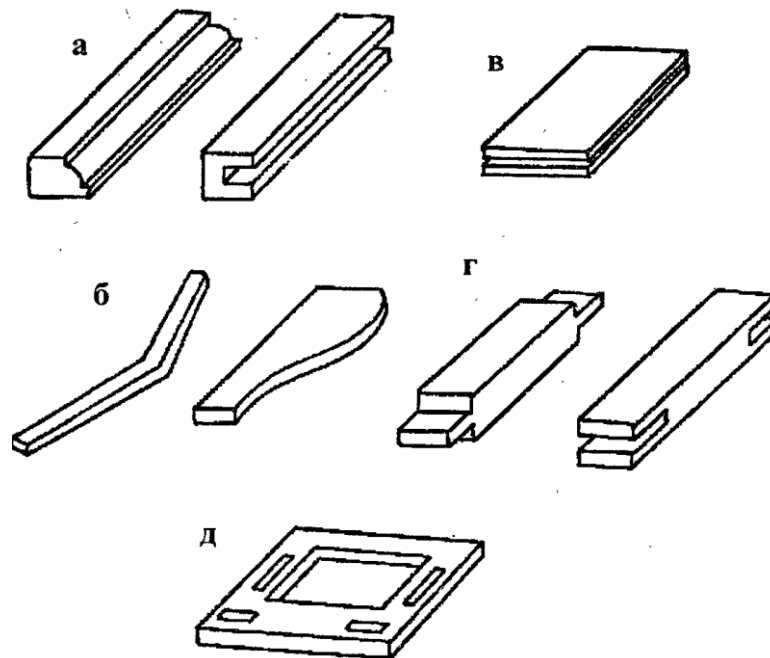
Види обробки на фрезерних верстатах: а – повздовжнє профільне фрезерування; б – криволінійне фрезерування; в – обробка по контуру; г – фрезерування шпильок; д – профільне фігурне фрезерування.
